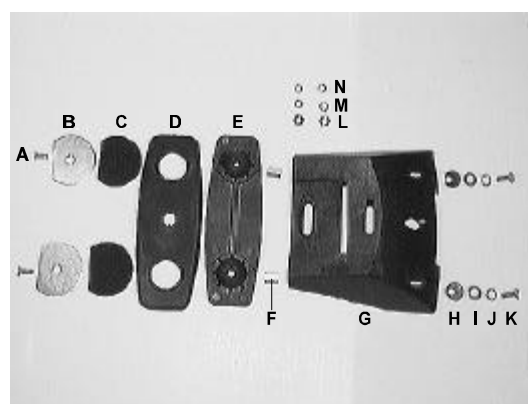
Komponenten für jede Halterung des Kit (permanente Befestigung)
